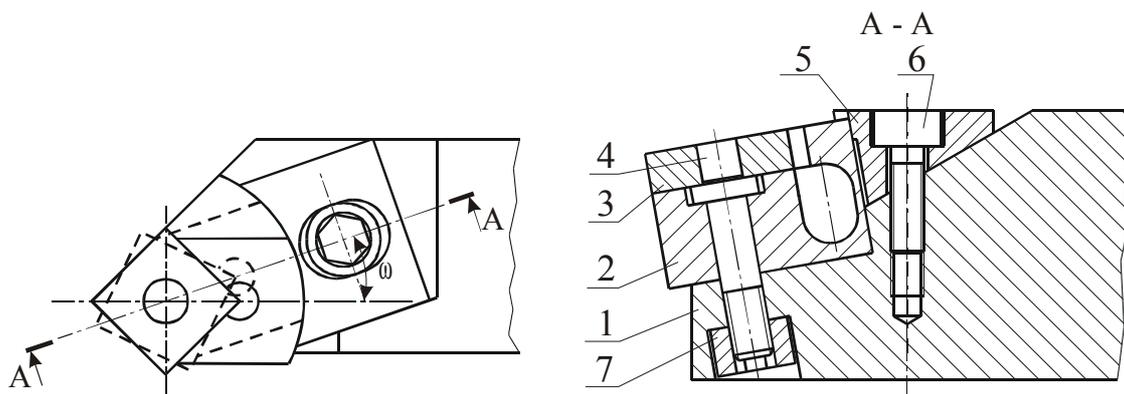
Универсальный токарный резец с поворотной рабочей частью
